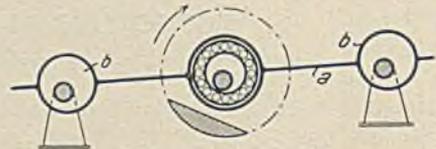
Aufbau des Universalschwingsiebes in Abb. 22.
